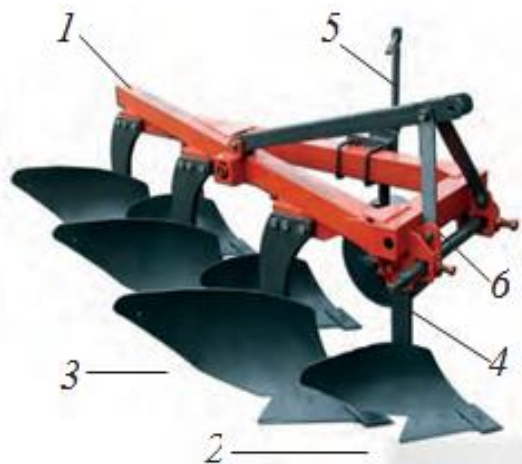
Конструкція ярусного плуга робочою поверхнею швидкісного типу.
